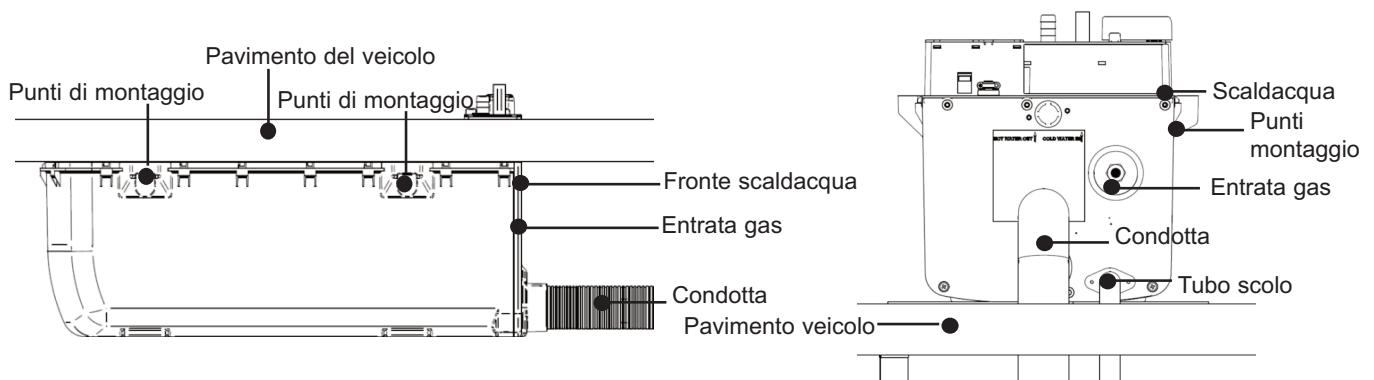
Installazione completata – modelli sotto il pavimento Fig. 33 Installazione completata – modelli a bordo
